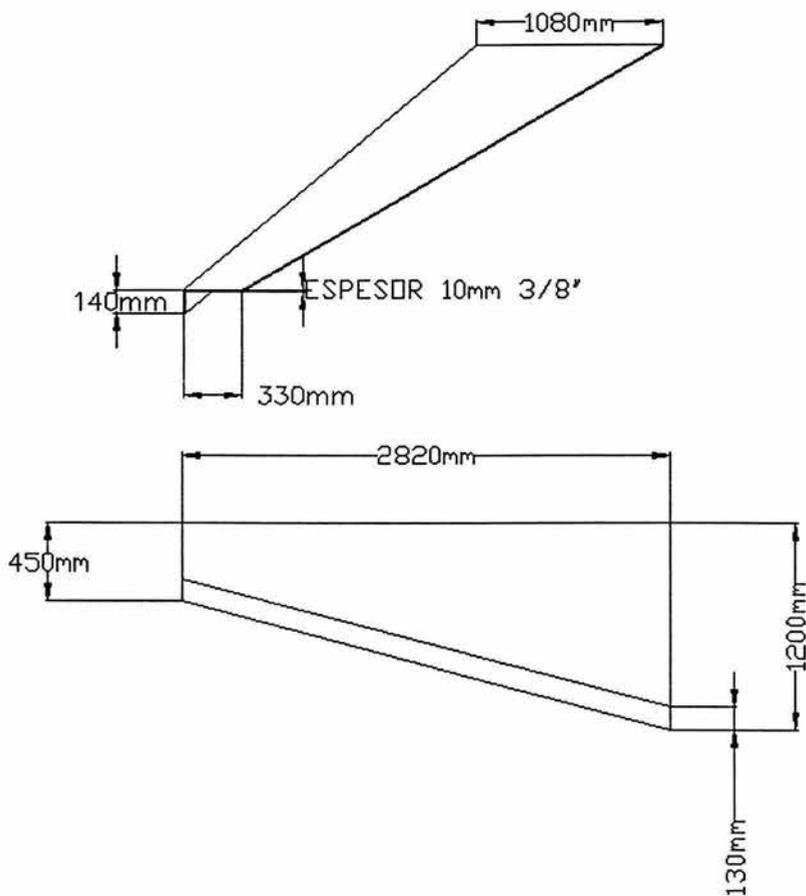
Ejemplo de dimensionamiento de la placa de sector sin sujeción para su corte y doblado.
